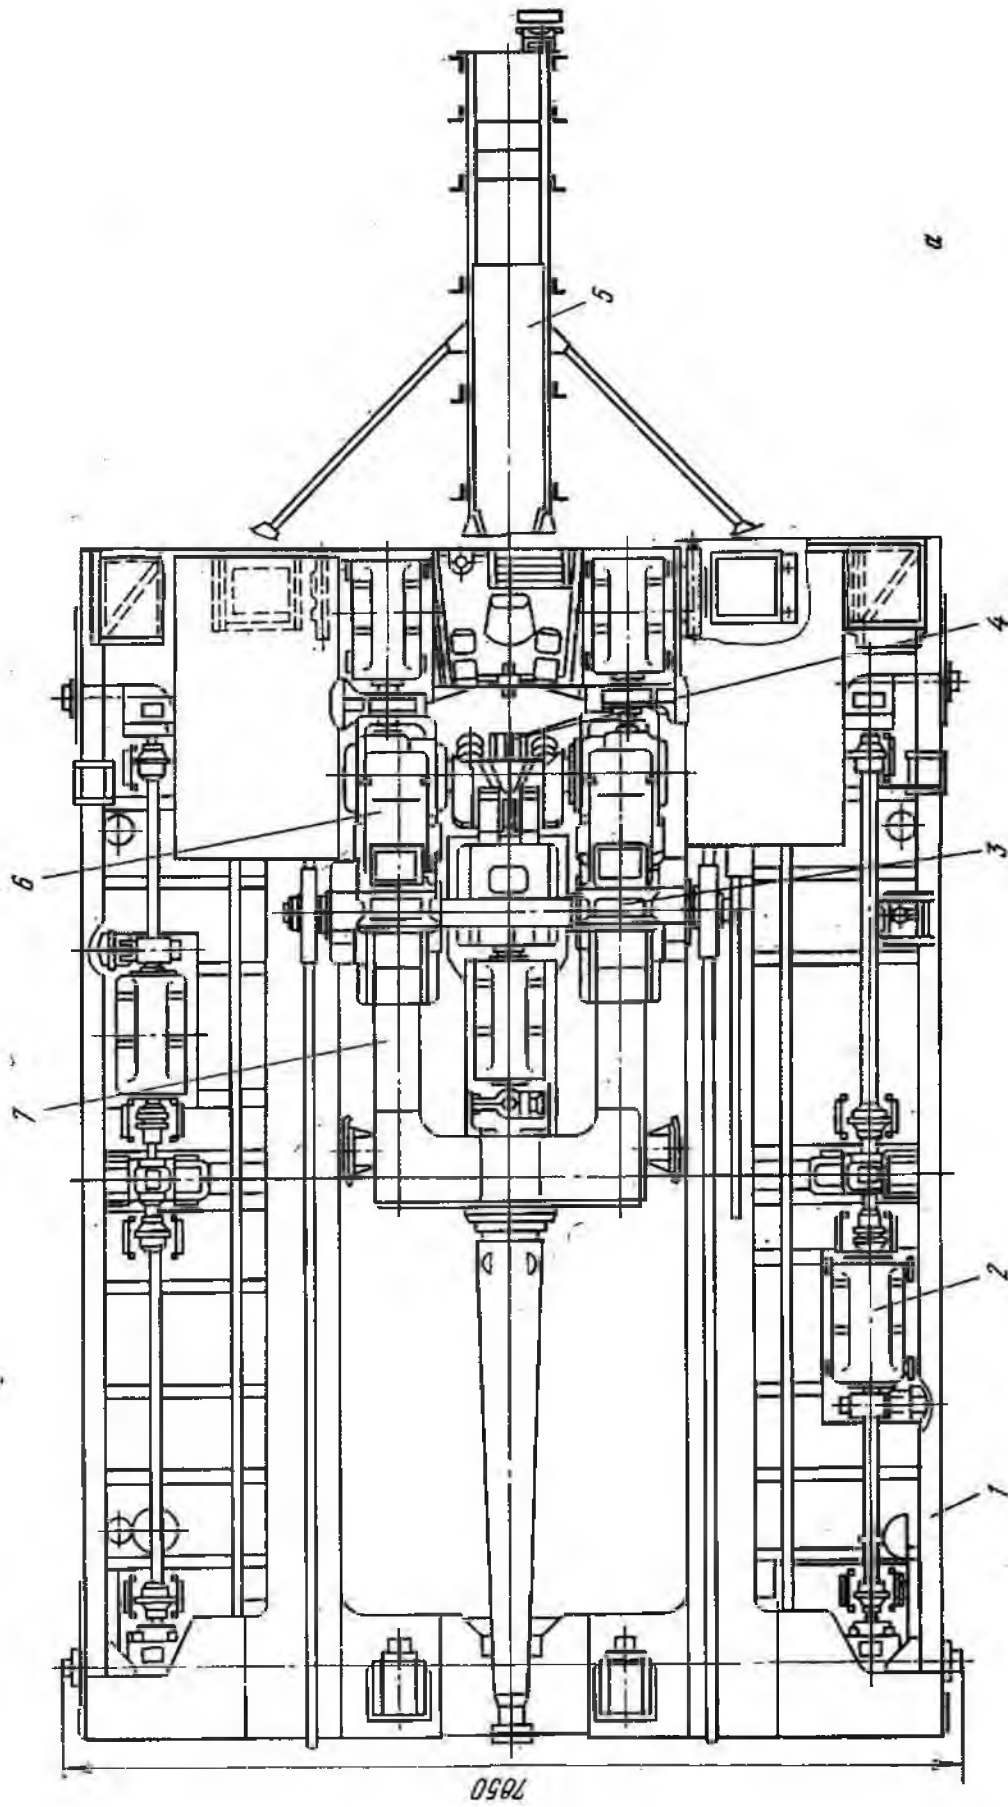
Напольно-завалочная машина (вид сверху)
